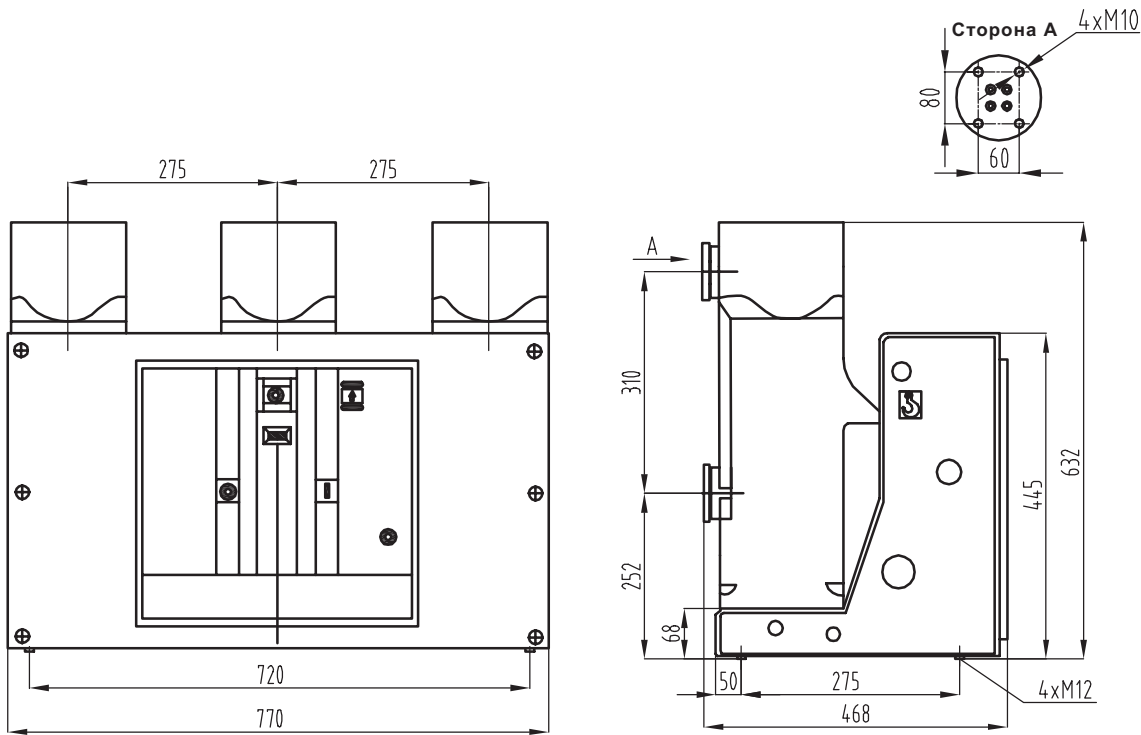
Габаритный размер выключателя ВВ-12 стационарного исполнения для ячейки шириной 1000 мм
